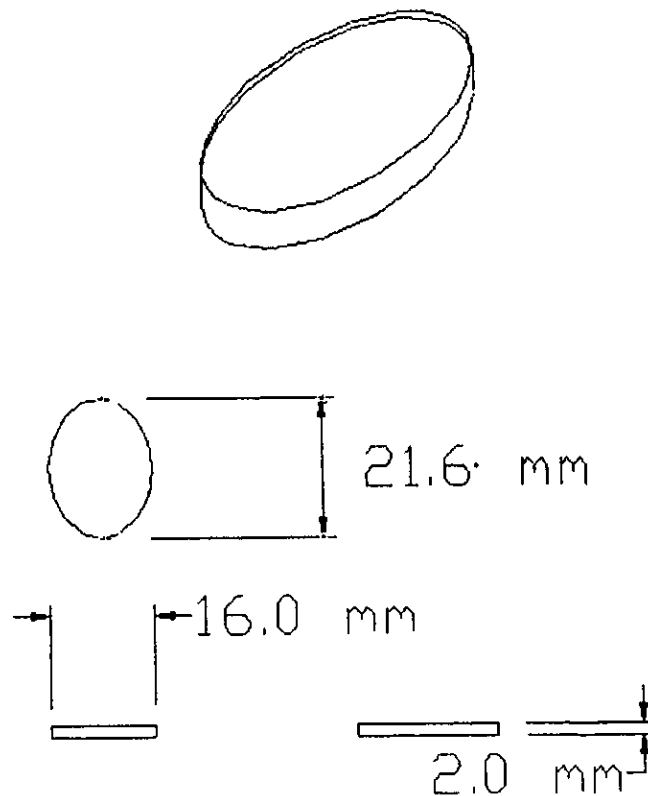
Dibujo y dimensiones de pastilla cosmética
